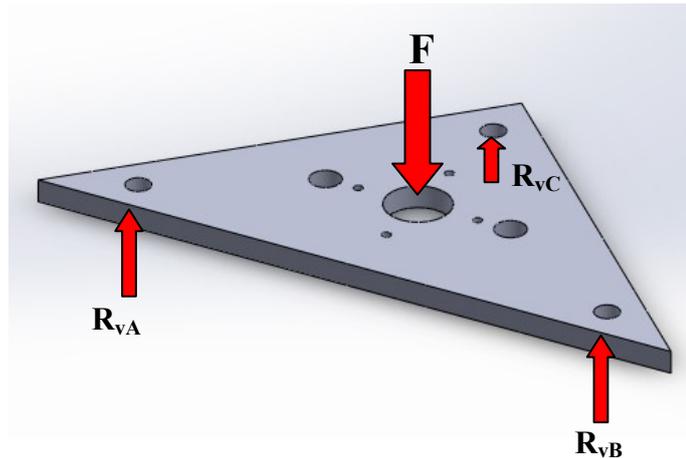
Dimensi plat bawah *mold O-ring
